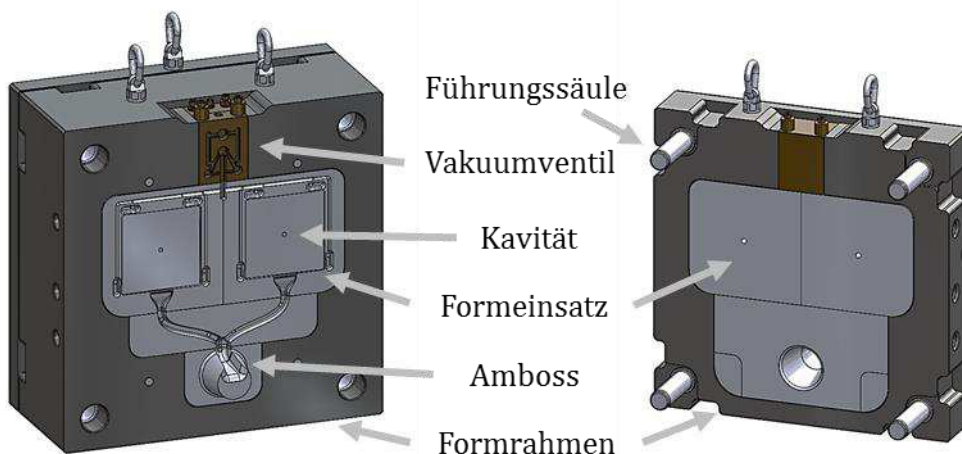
Das Druckgießwerkzeug und seine Hauptkomponenten.
